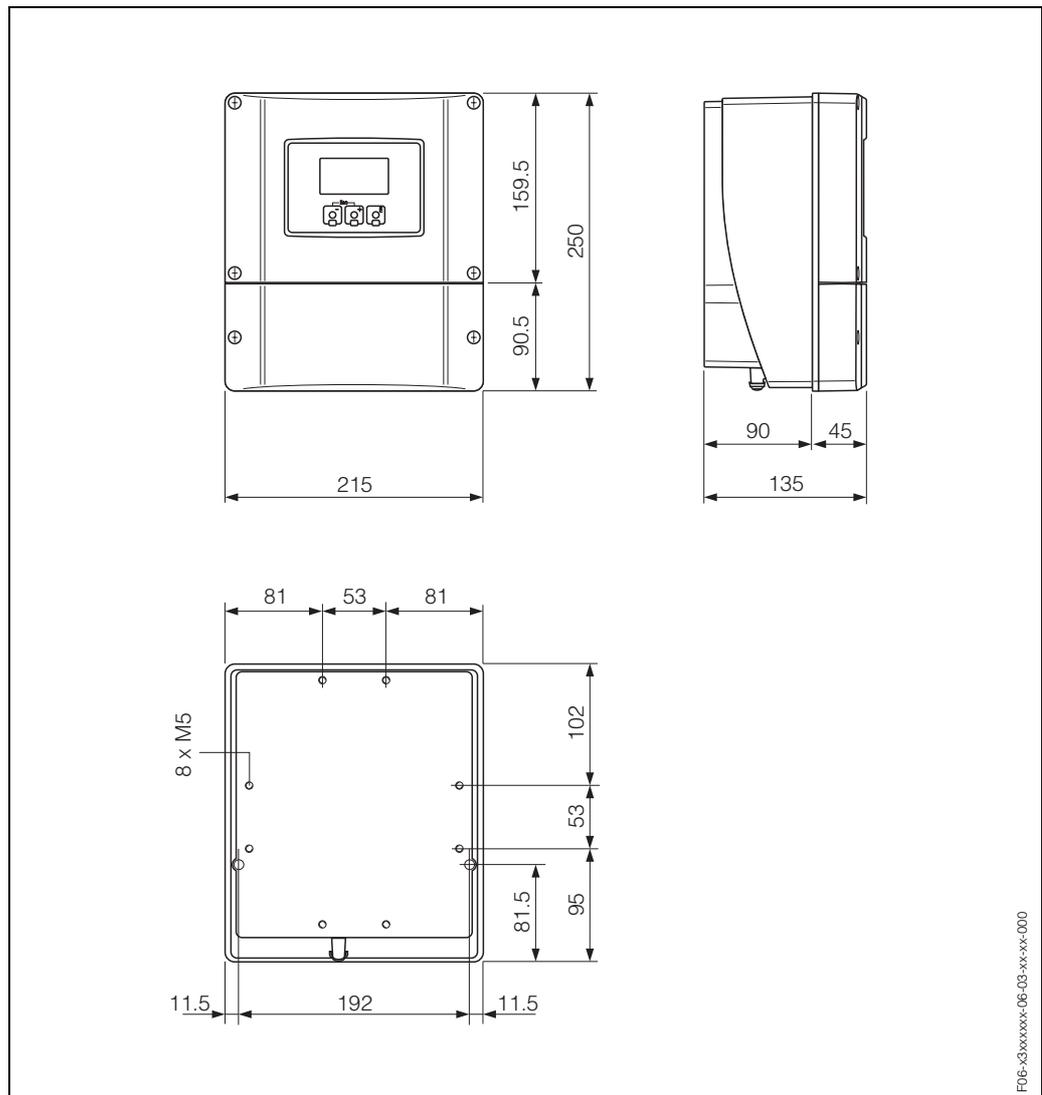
Abmessungen Wandaufbaugehäuse (Schalttafeleinbau und Rohrmontage → Seite 44)
